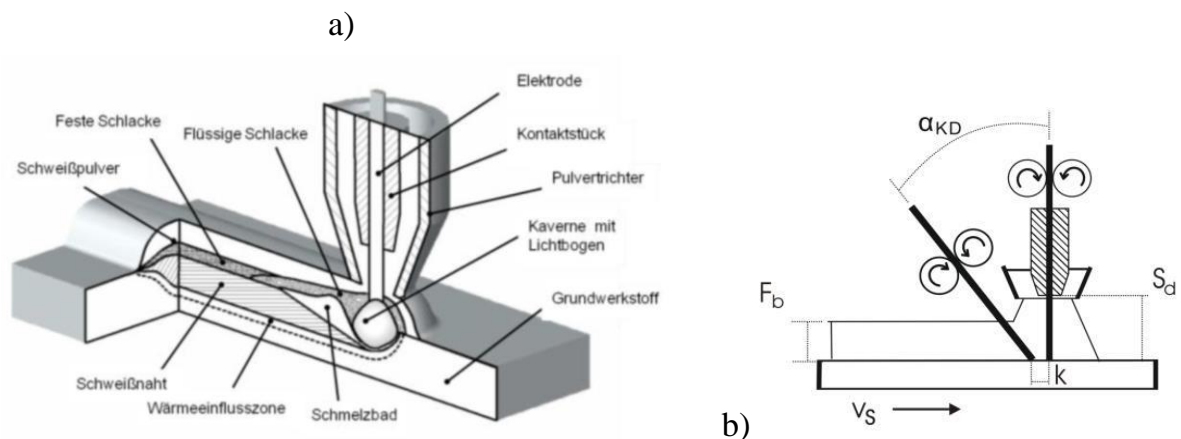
a) Verfahrensprinzip des UP-Schweißens, b) Schematische Darstellung des UP-KD-Schweißens
